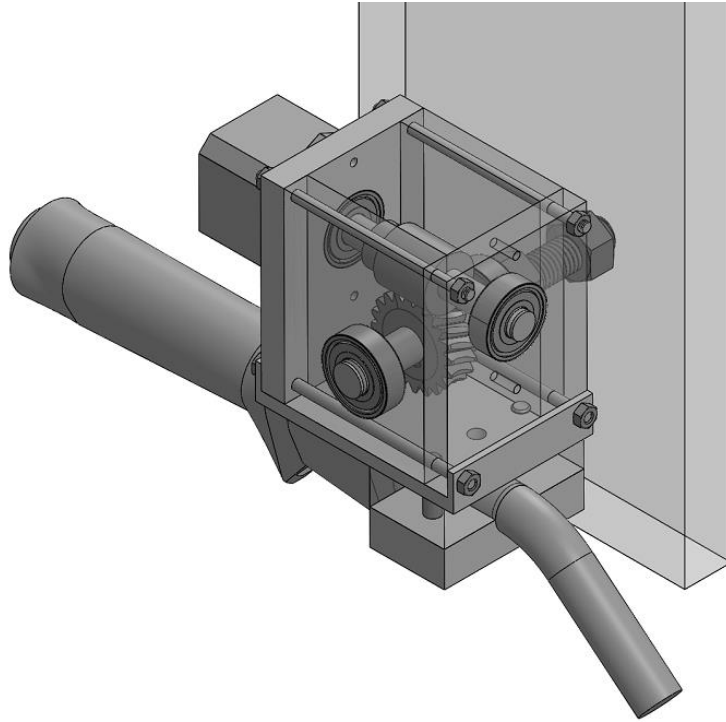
Montagem final do mecanismo de soldadura.
